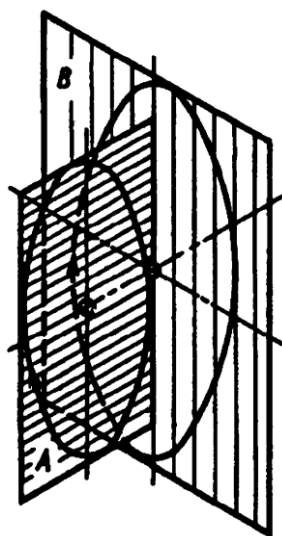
Схема фрезерування тіл обертання торцевими фрезами
